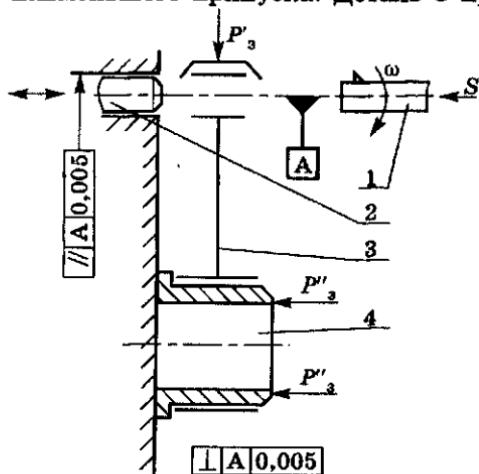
Схема установки и базирования шатуна при растачивании отверстия в верхней головке: 1 — шпиндель станка; 2 и 4 — оправки; 3 — деталь
